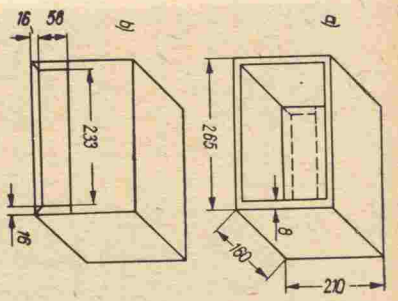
Maßskizze für das Gehäuse aus 8 bis 10 mm starkem Holz
